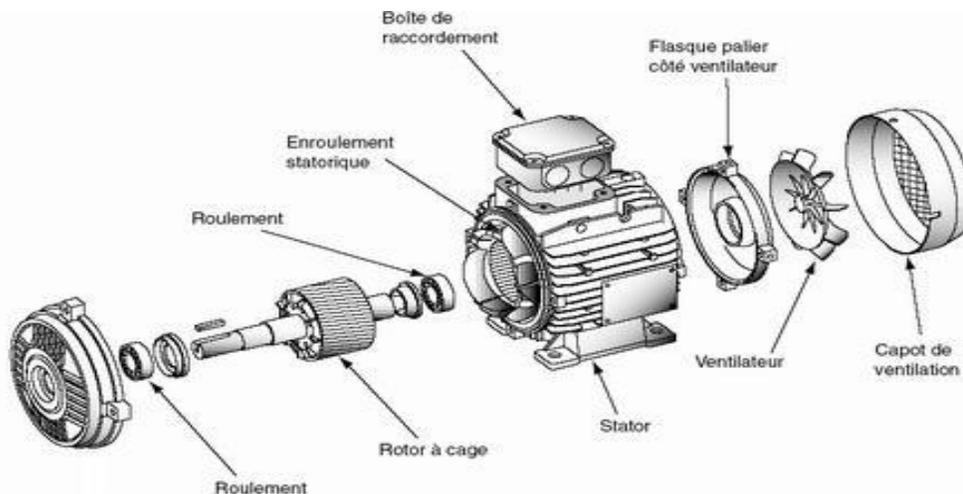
Moteur asynchrone à cage d'écureuil [14].
